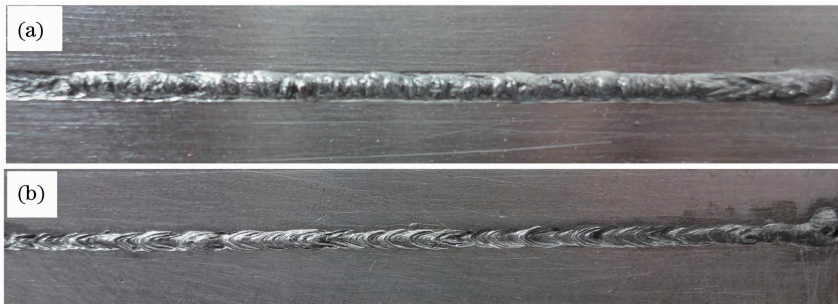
焊缝表面,左端为收焊处。(a)焊缝正面;(b)焊缝背面
